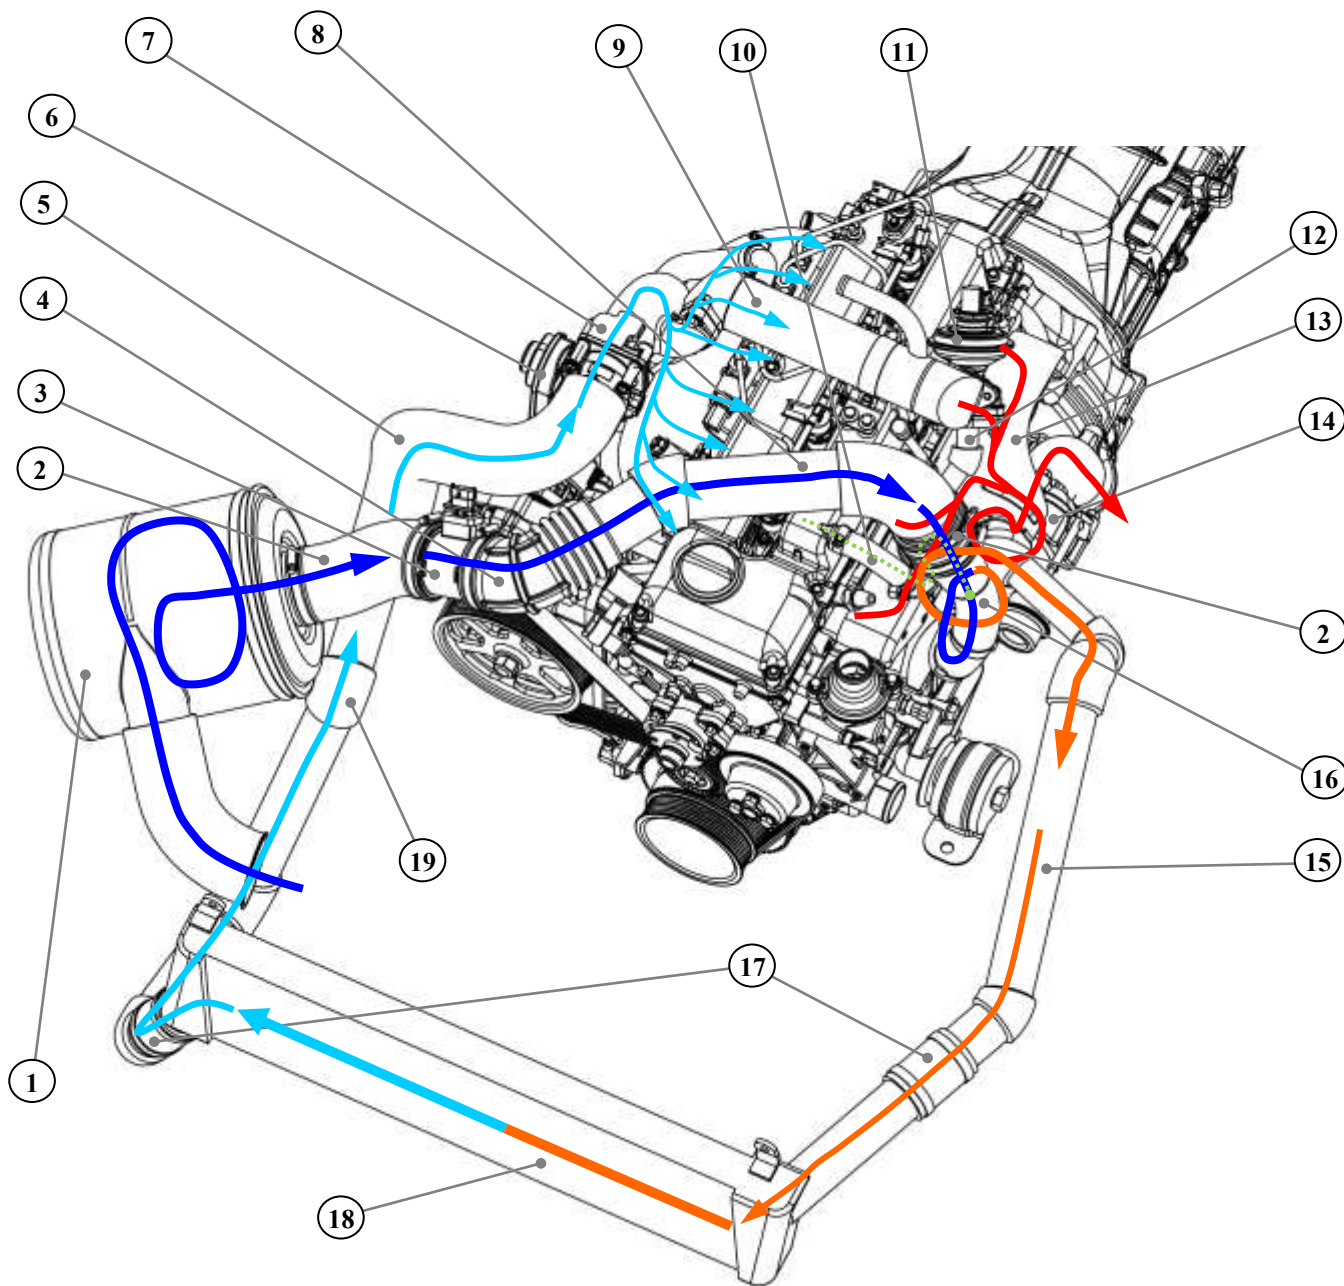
Общий вид системы подачи воздуха и выпуска ОГ:
